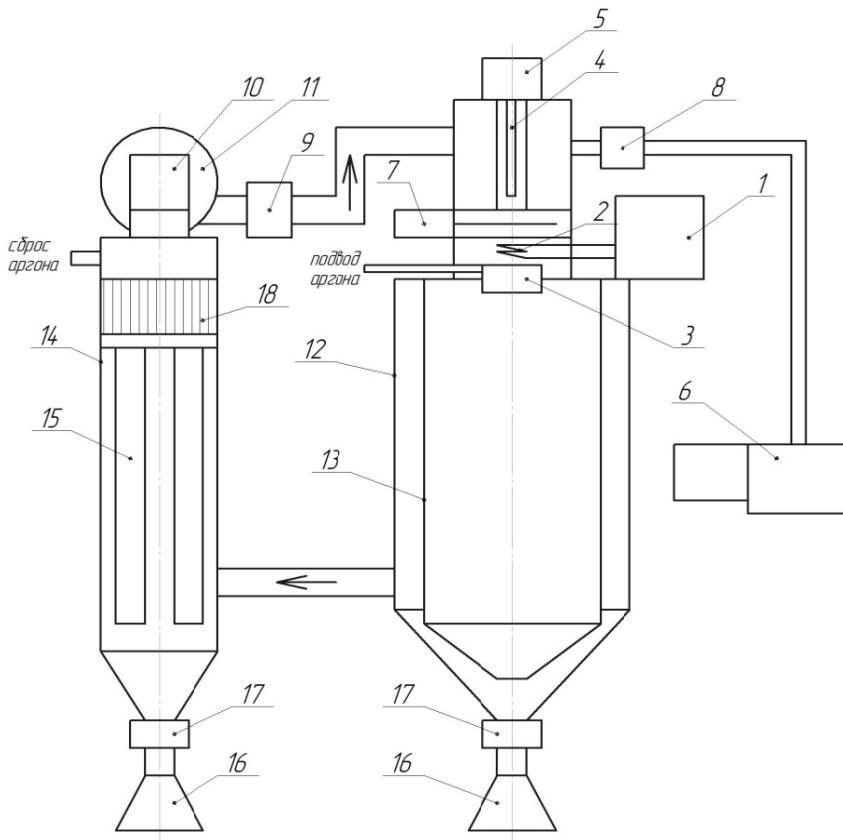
Схема УРМ-002: 1 – плавильный агрегат; 2 – индуктор; 3 – распылительная форсунка; 4 – заготовка; 5 – привод подачи заготовки; 6 – вакуумный насос; 7 – вакуумный затвор; 8, 9, 10 – вакуумные клапаны; 11 – циркуляционный вентилятор; 12 – камера распыления; 13 – экран; 14 – фильтровально-охладительная камера; 15 – рукавный фильтр; 16 – емкость для сбора порошка; 17 – блок вентиляй; 18 – охладитель аргона
